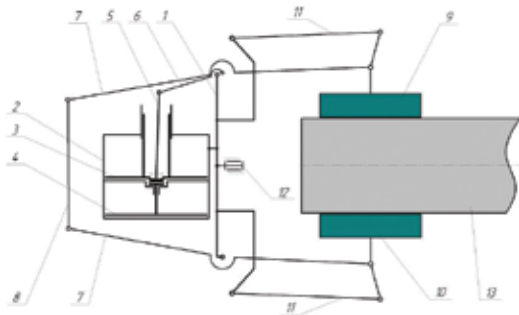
Структурная схема механизма тормозного блока 740. 1 — корпус; 2 — цилиндр рабочего и стояночного приводов; 3 — поршень рабочего привода; 4 — поршень стояночного пневмопривода; 5 — качающийся шток; 6 — поводок; 7 — рычаги-клещи; 8 — регулятор зазора между накладками и диском; 9, 10 — колодки с закрепленными на них фрикционными накладками; 11 — жесткие звенья, образующие параллелограммные контуры; 12 — подвес к раме тележки; 13 — тормозной диск
